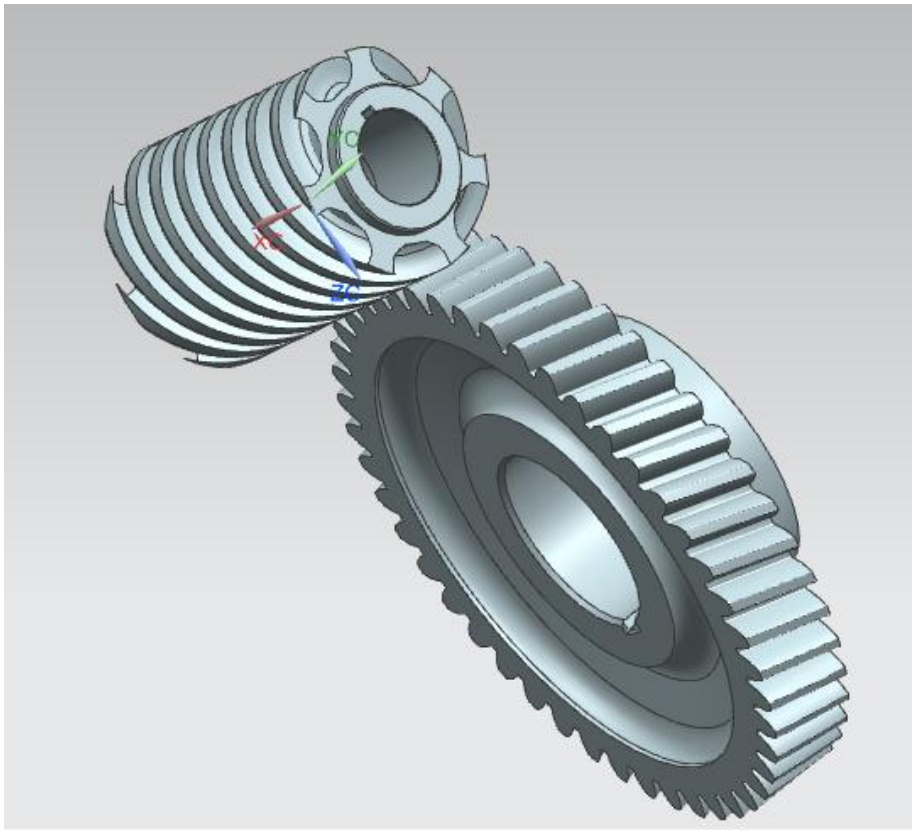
Визуализация наладки инструмента червячного типа со сплошными винтовыми режущими кромками на станке в модуле “Сборка” системы NX
